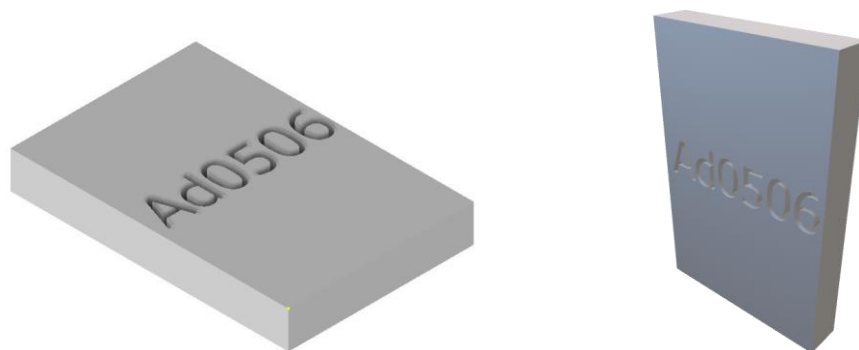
Τρισδιάστατη απεικόνιση αποστολής 34
